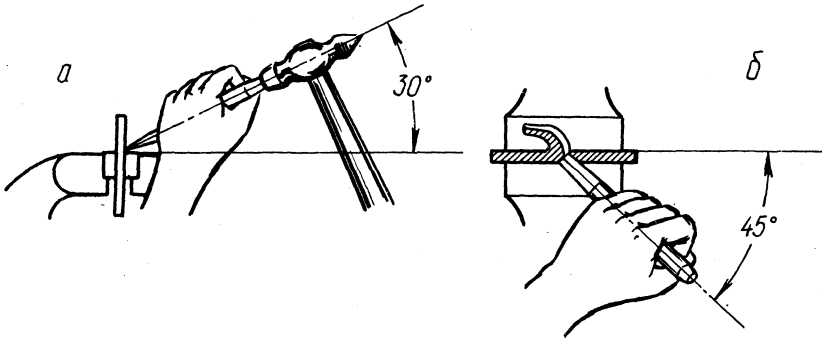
Углы наклона зубила при рубке листового материала в тисках: а — к обрабатываемой поверхности; б — к заготовке
